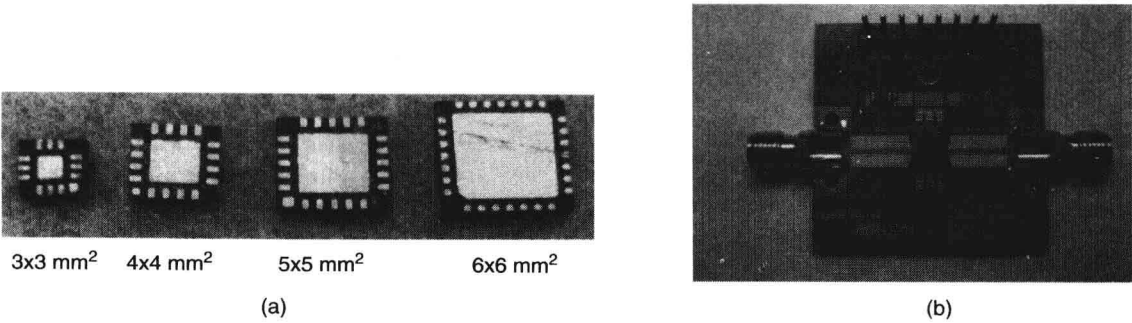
(a) 高性能 PQFN 塑料封装; (b) 用于 PQFN 封装测试的 PCB
